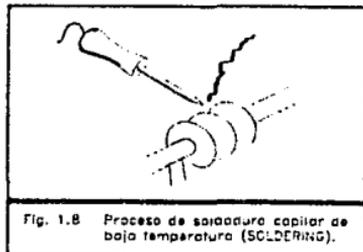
Proceso de soldadura capilar de baja temperatura (SOLDERING).
